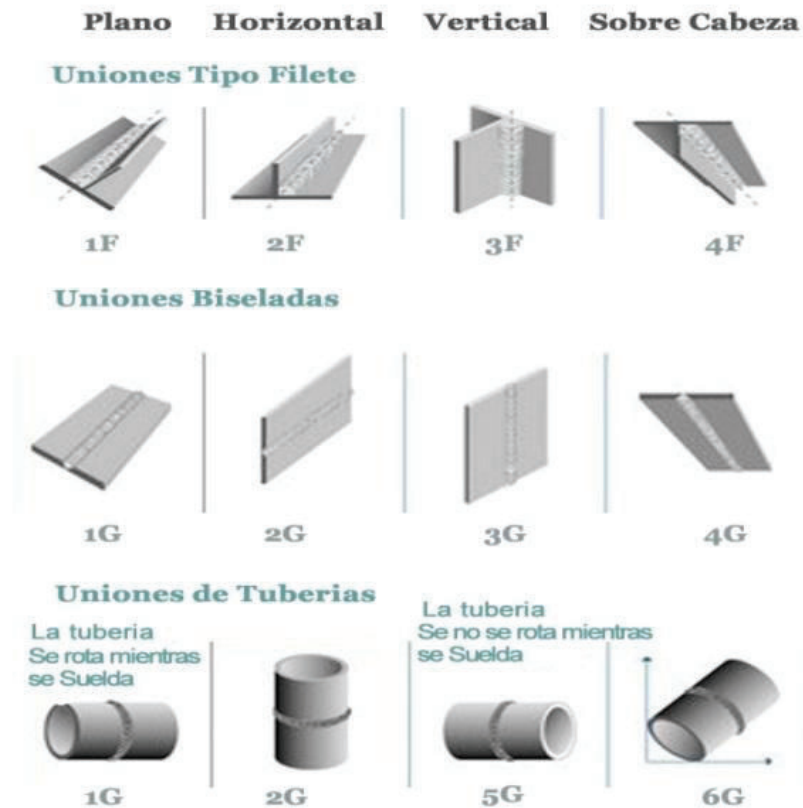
25 Posiciones de soldadura¹⁶
